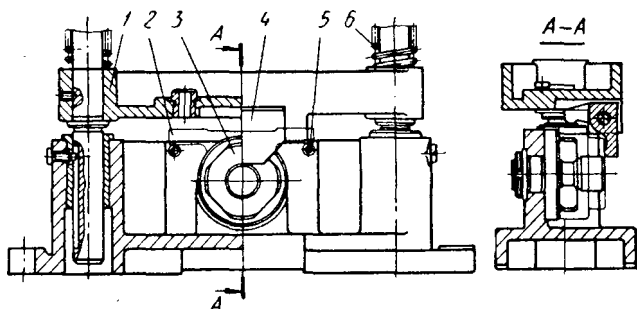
Приспособление к многошпиндельной головке для обработки отверстий в корпусах подшипников
